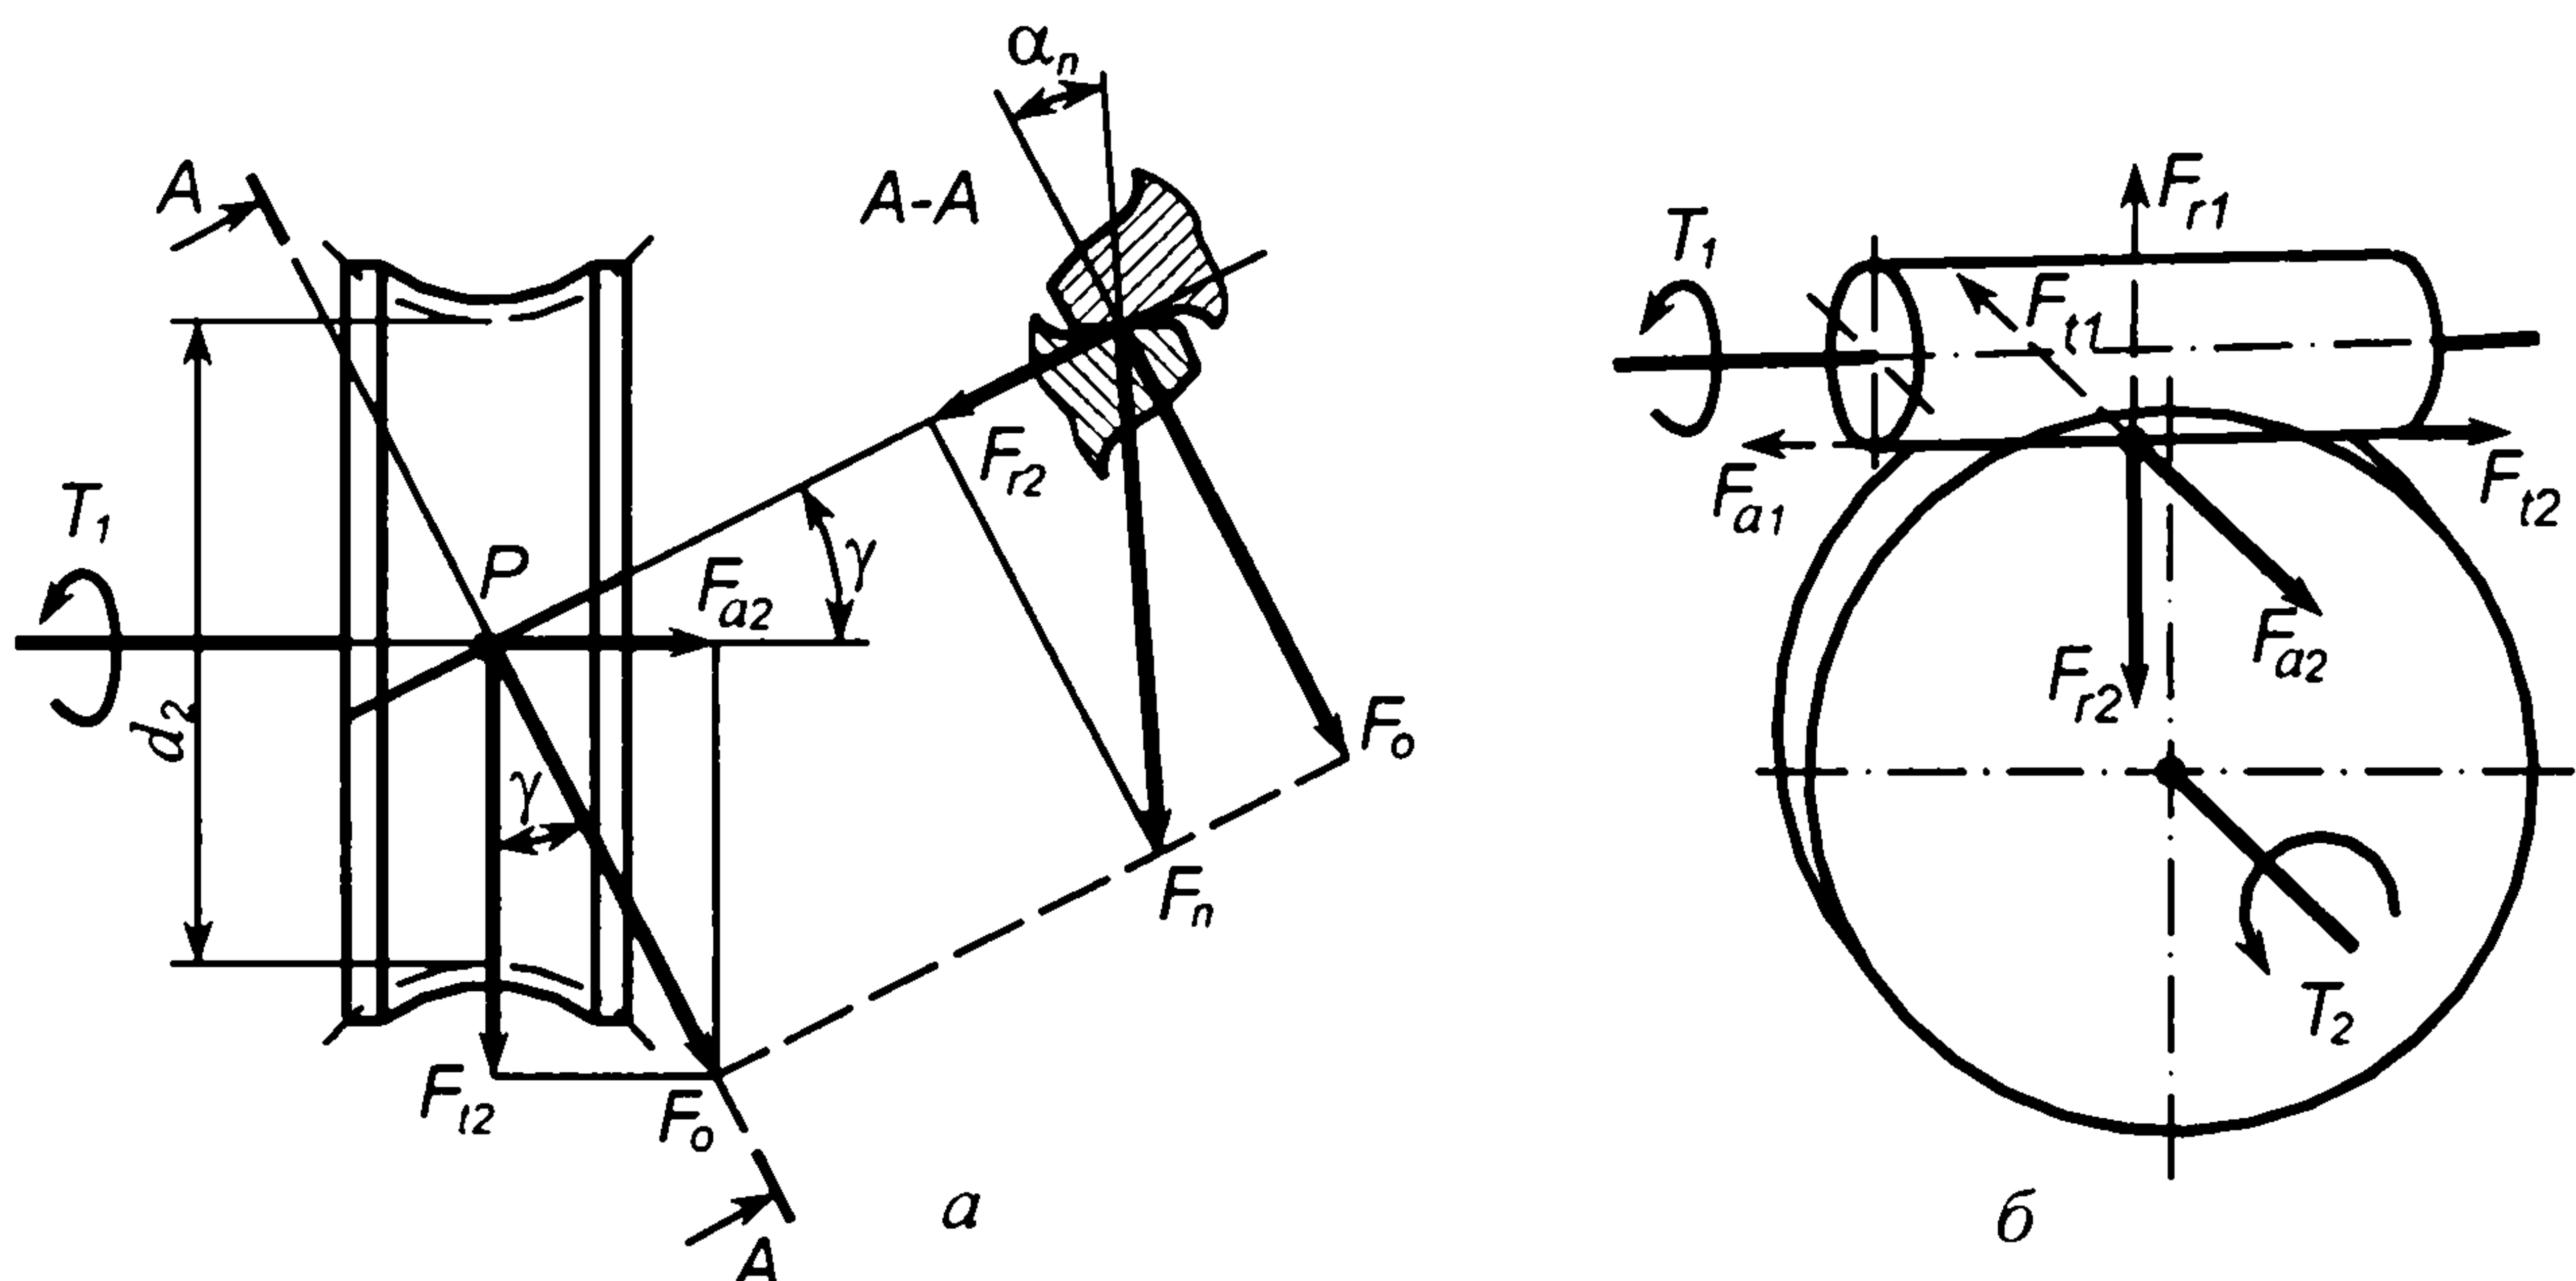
Зусилля на зубці черв'ячного колеса та витки черв'яка
